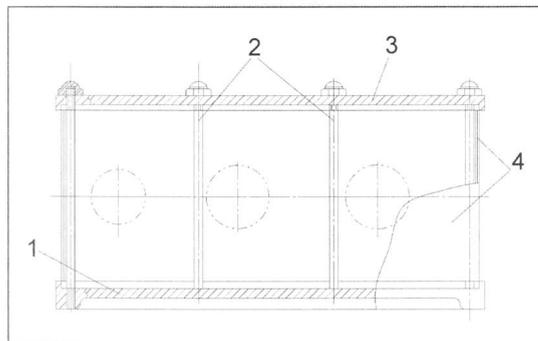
Навитой корпус до затяжки шпилек после корпуса из ленты: 1 — основание, 2 — шпилька, 3 — крышка, 4 — стенки корпуса из ленты.
